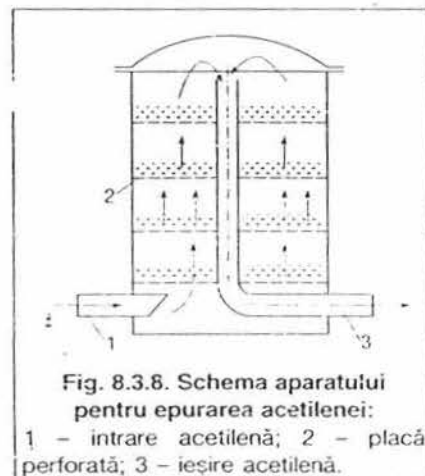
Schema aparatului pentru epurarea acetilenei:
